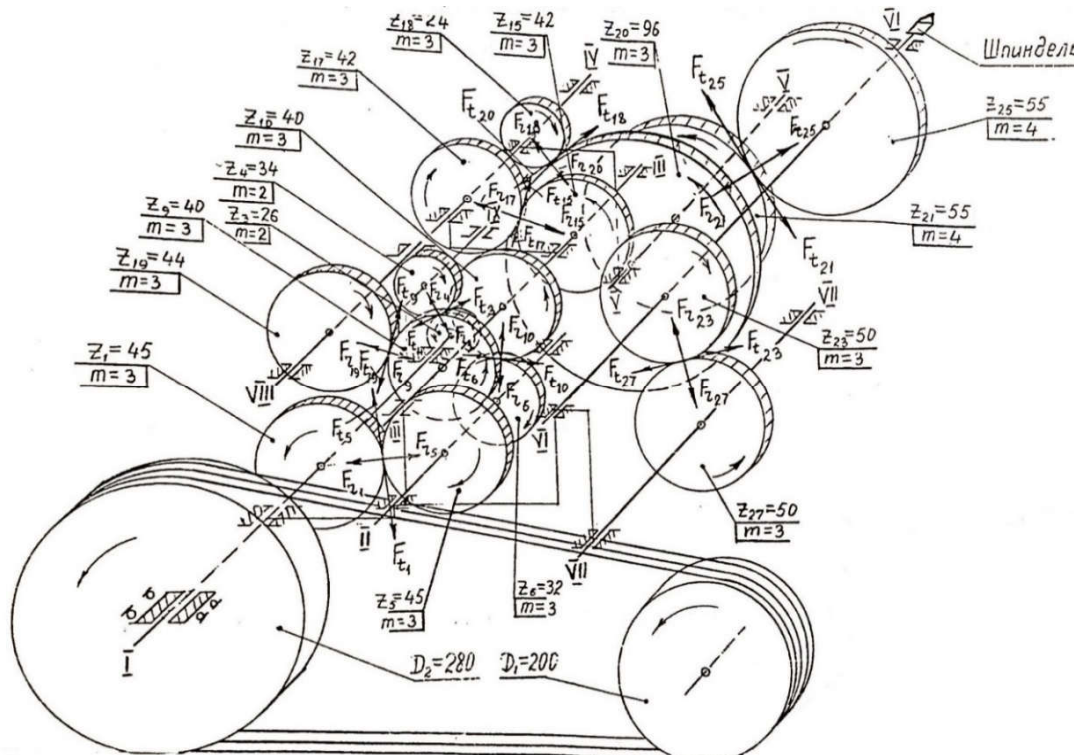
Силы, действующие на зубчатые колеса главного привода токарного станка 1К625:
